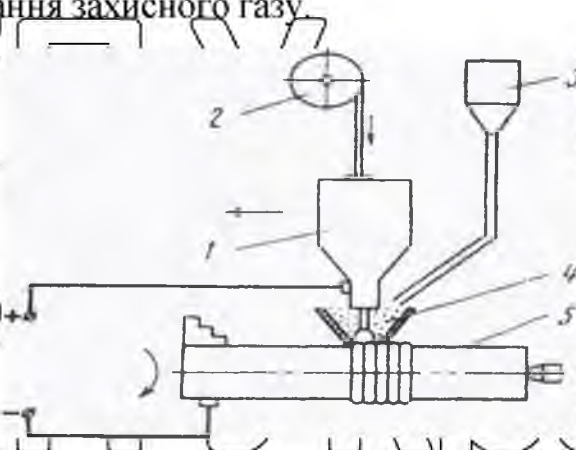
Конструктивна схема наплавлення електродугового з використанням флюсу:
